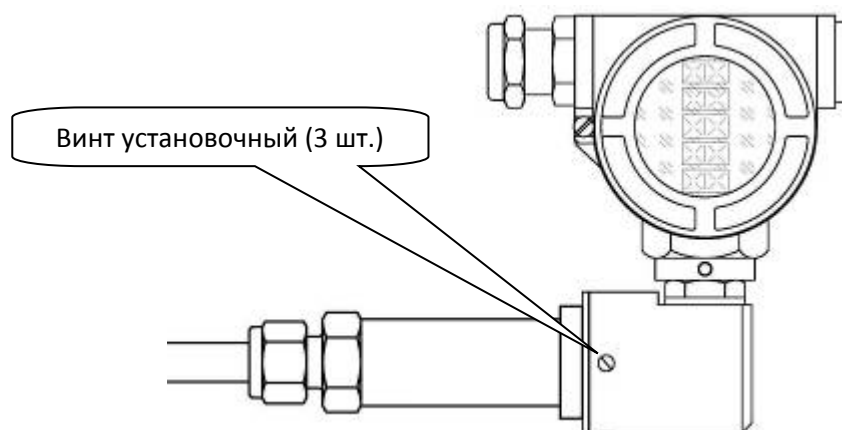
Расположение винта установочного на крышке преобразователя
